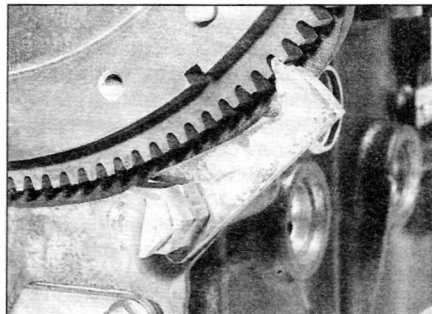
Используйте самодельный инструмент, аналогичный показанному, чтобы застопорить зубчатый венец маховика и предотвратить проворачивание коленчатого вала
